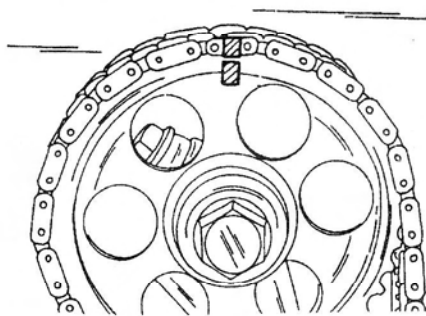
Маркировка звездочки распределительного вала и цепи перед снятием деталей.
